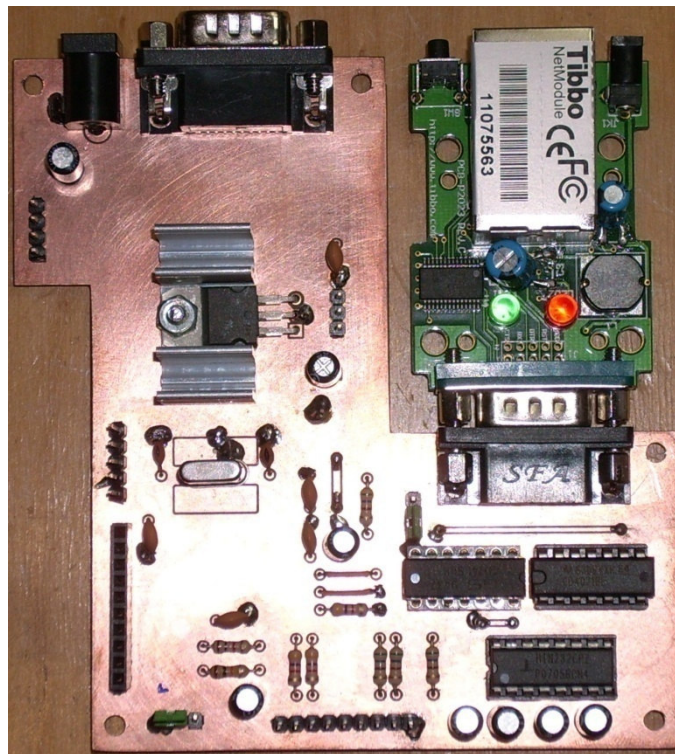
Face superior da PCB do Módulo Cadastramento montado com o Conversor Tibbo
